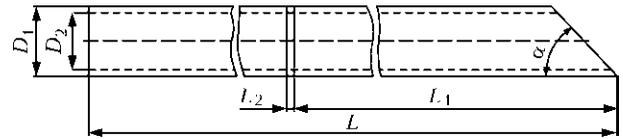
Схема модельного образца полимерной трубы, сваренного с использованием процесса стыковой сварки
